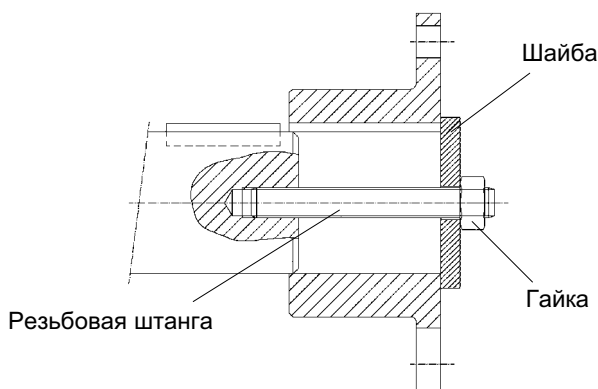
Натяжка ступицы с резьбовой штангой
